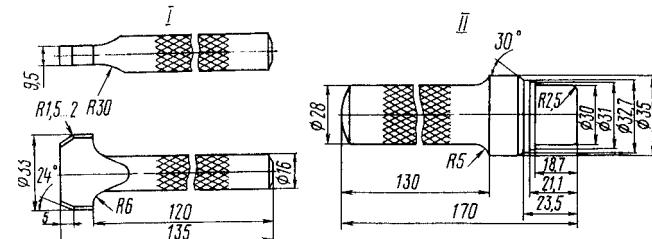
Оправки для установки заглушки в шатунной шейке коленчатого вала: I - оправка для развалцовки; II - оправка для запрессовки
